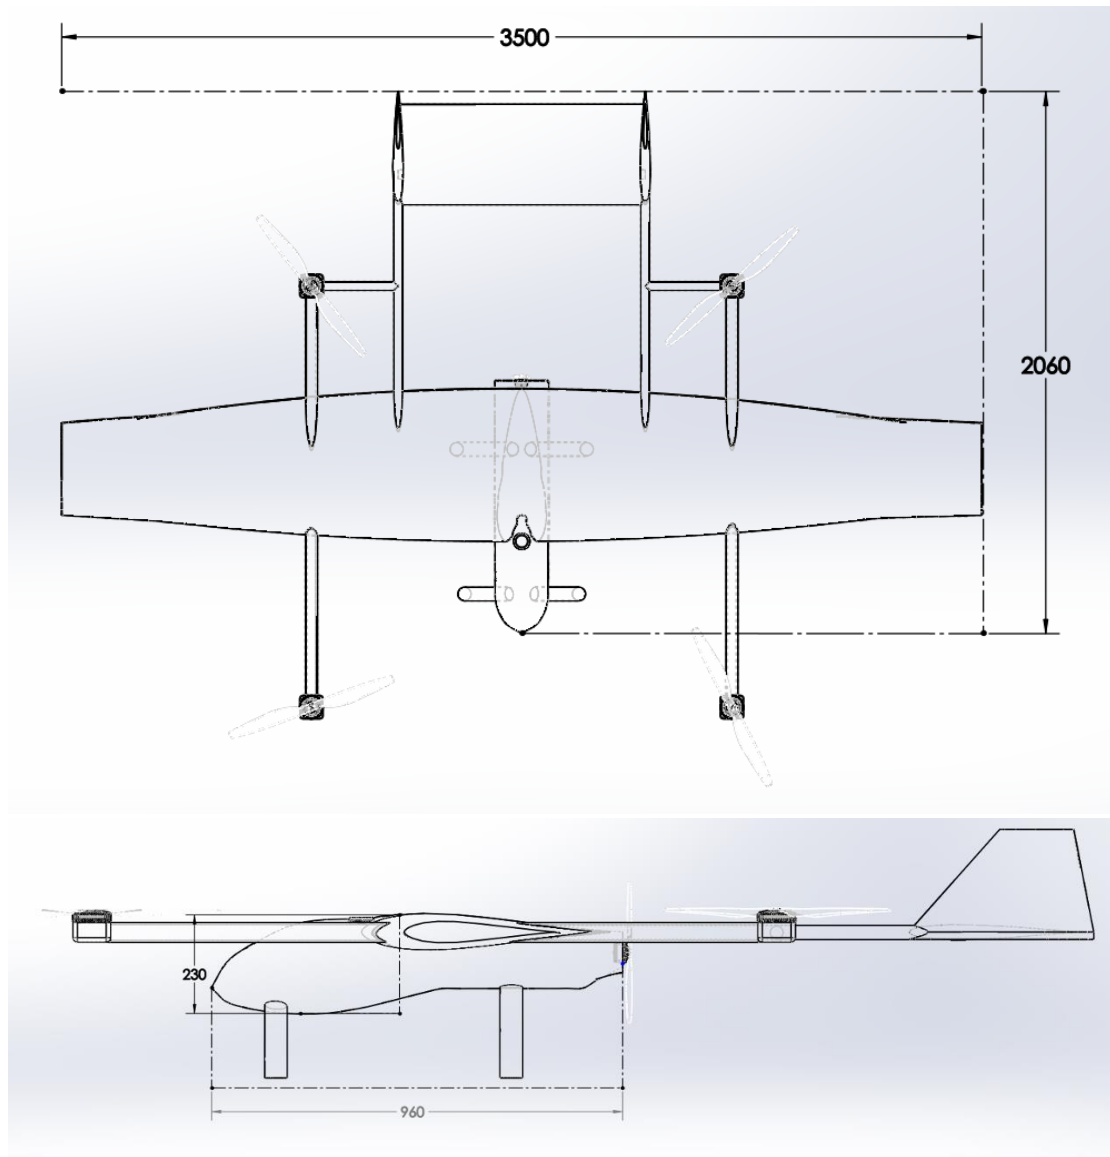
และ 9 รูปแบบ Drawing มุมมอง Top View และ Side View ตามลำดับ
